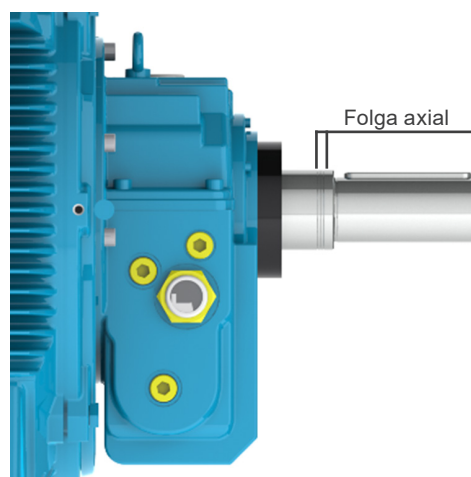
Folga axial em motor equipado com mancal de deslizamento
